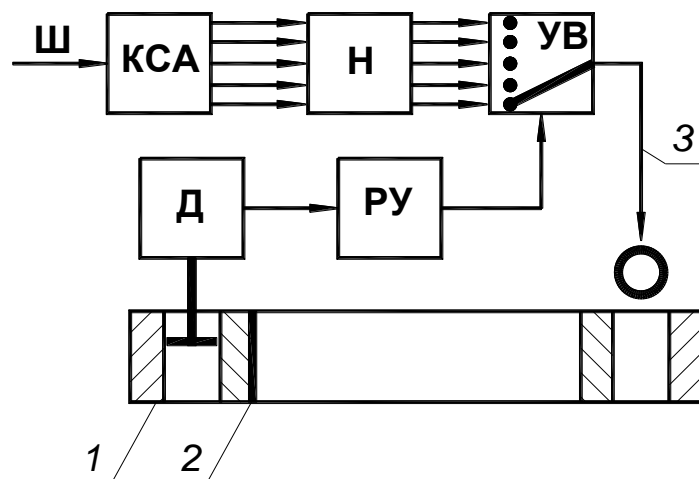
Схема автоматической сборки шарикоподшипников методом регулирования [13]
